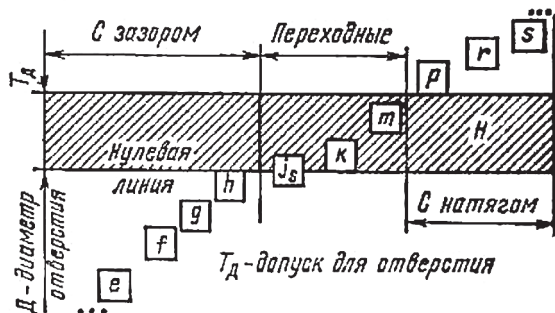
Поля допусков для обеспечения посадок с натягом
